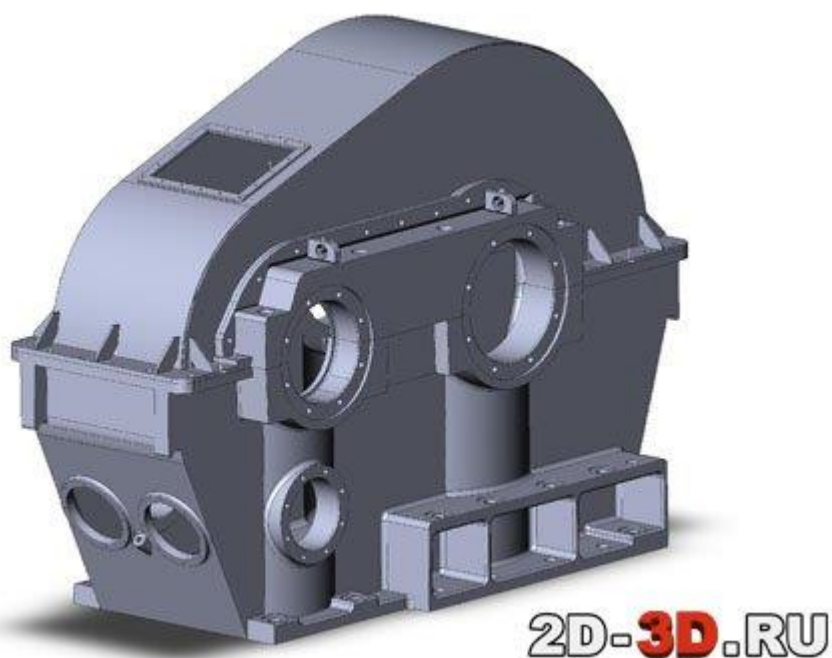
«Корпус редуктора лебедки подъема»
